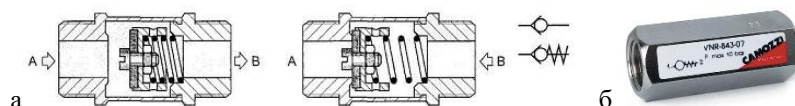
Обратный клапан: а – конструкция и условное графическое обозначение на схемах; б – внешний вид
